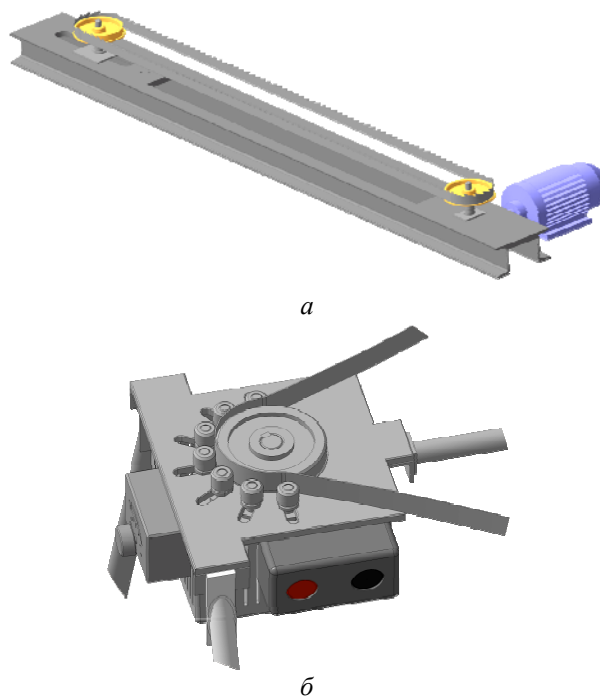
Установки для проведения упругопластического деформирования ленточной пилы:
